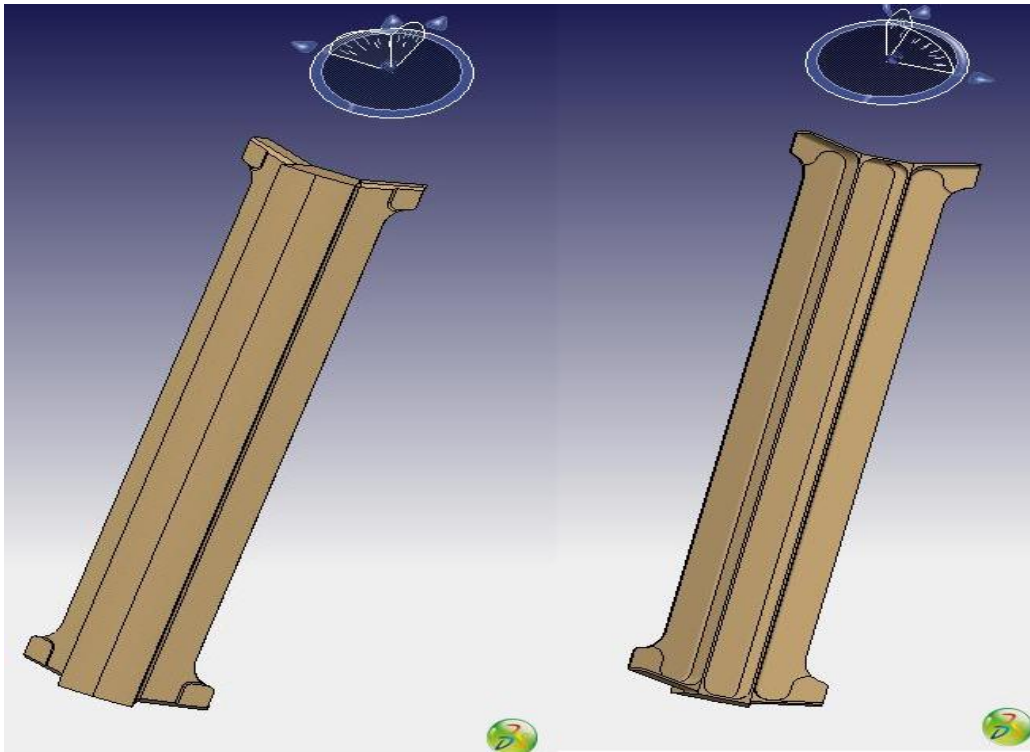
Proposta de alteração da viga central da estrutura.
